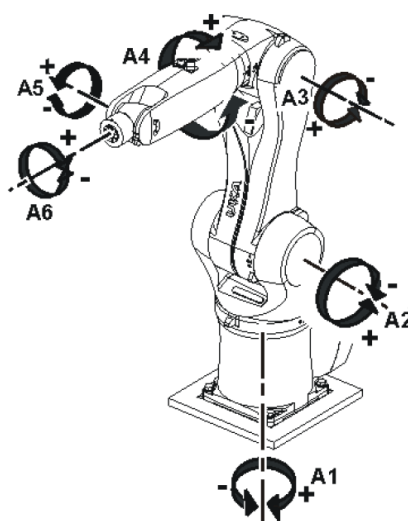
Hlavní komponenty – Kuka Agilus Kr 10 R110 [28]
